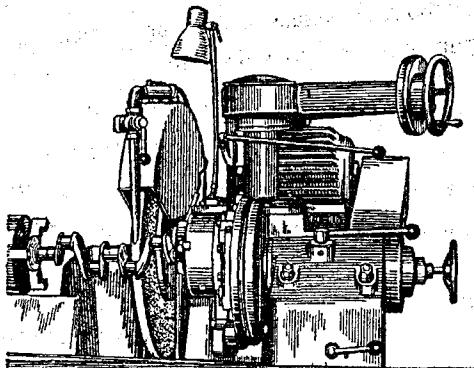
Шліфування шатунної шийки колінчастого вала на верстаті 3423.
